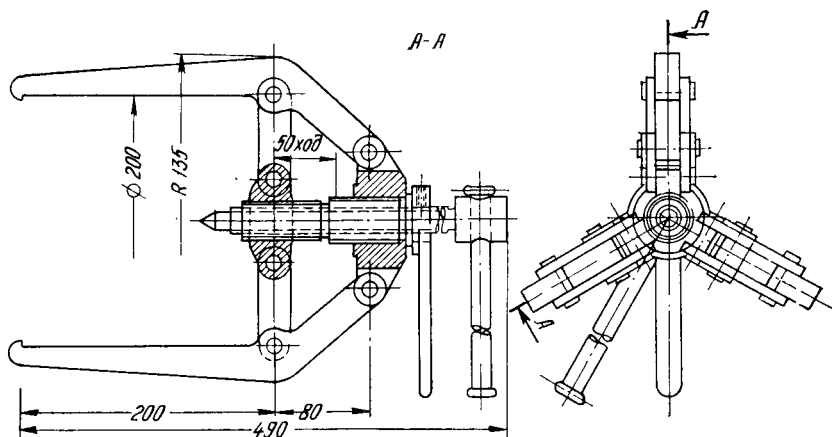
Приспособление для съема подшипников качения с вала электродвигателя
